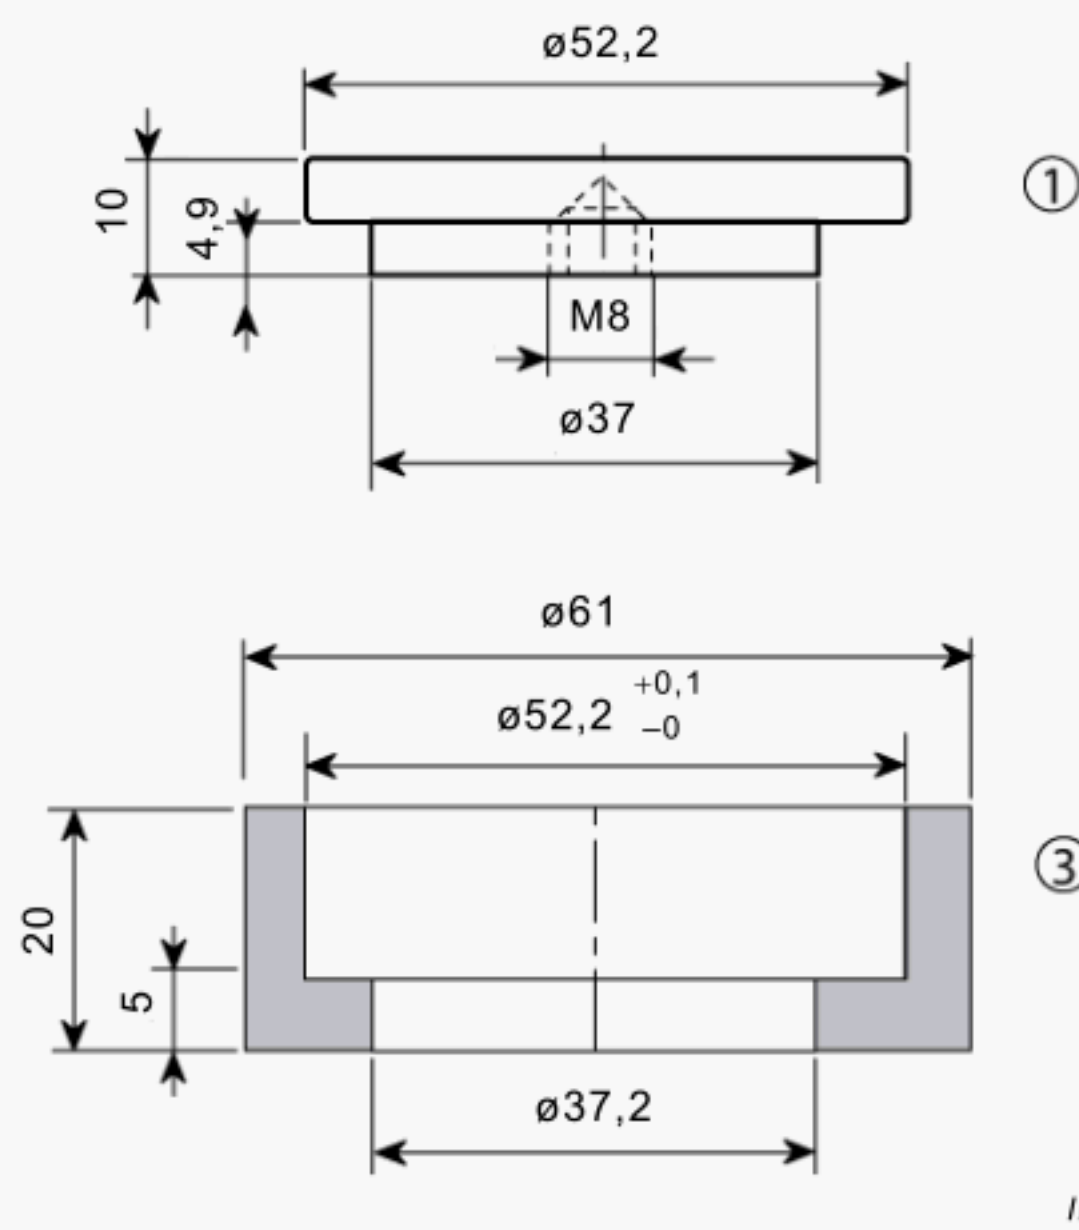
Pour tube rempli de mousse de 51 mm de diamètre
